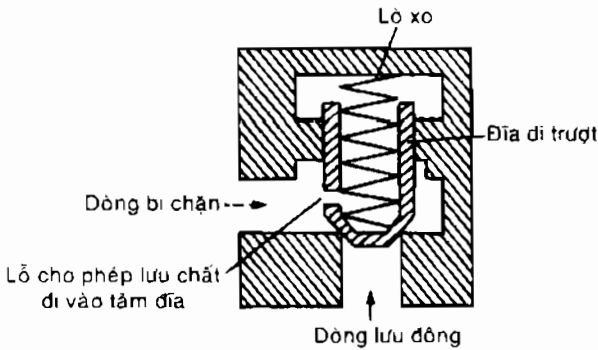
Valve vận hành nhờ valve dẫn hướng
